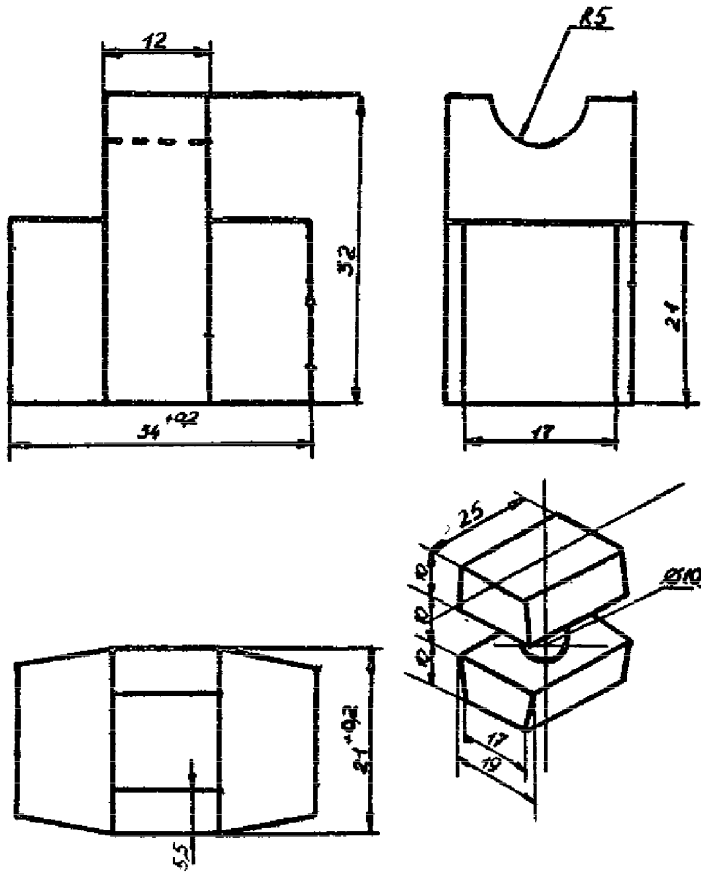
Пресс-форма для изготовления образца (пуансон).
